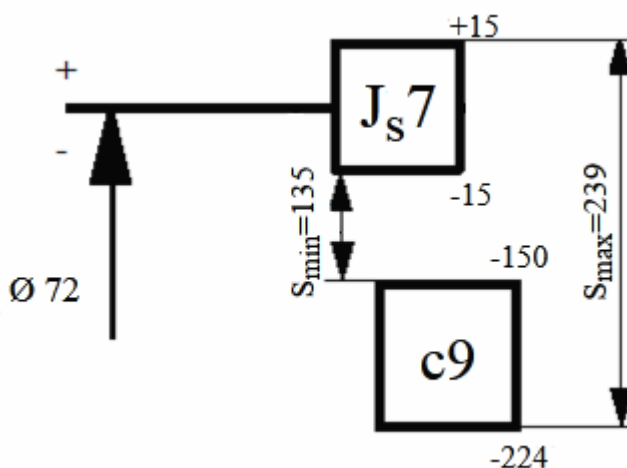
Выбор посадки для сопряжения крышки и отверстия корпуса
